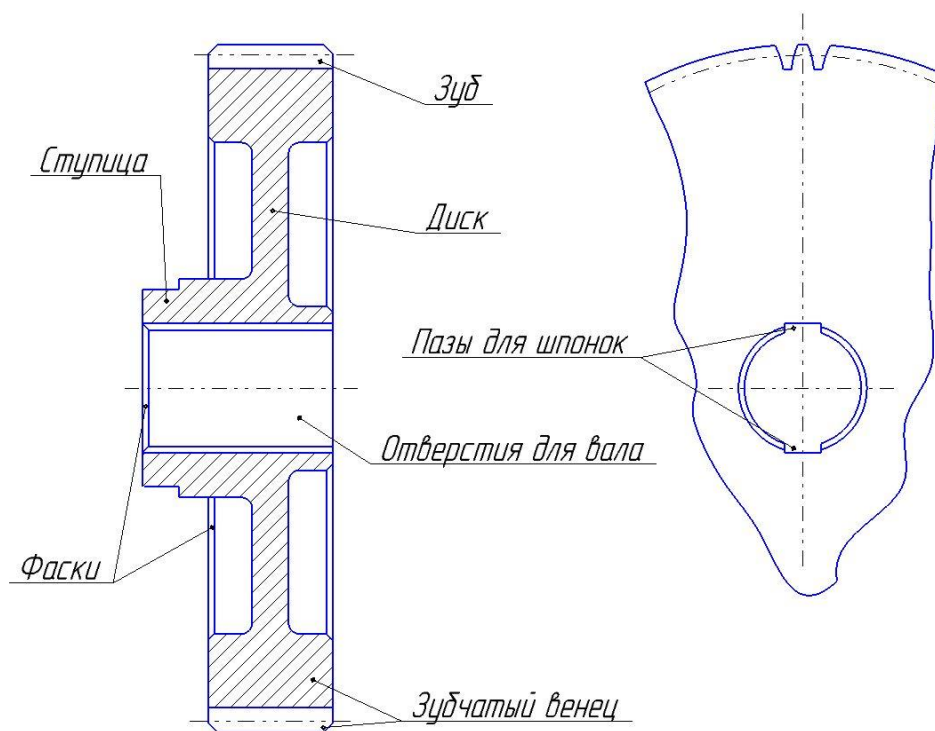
Основные конструктивные элементы зубчатого колеса
